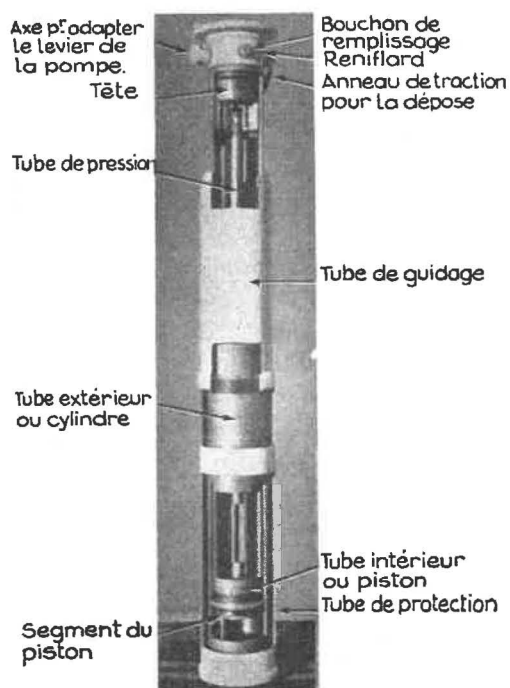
Vue d'ensemble de l'étauçon Polar.
